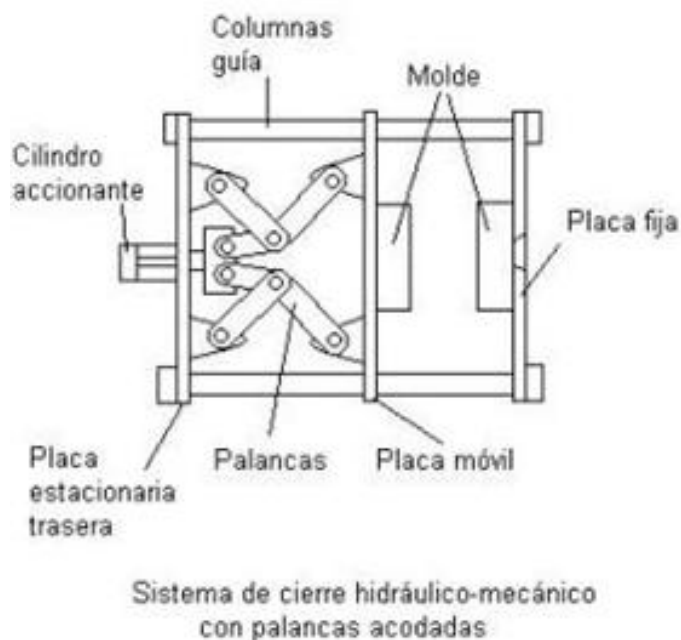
Partes principales que forman el sistema de cierre hidráulico con palancas acodadas.
